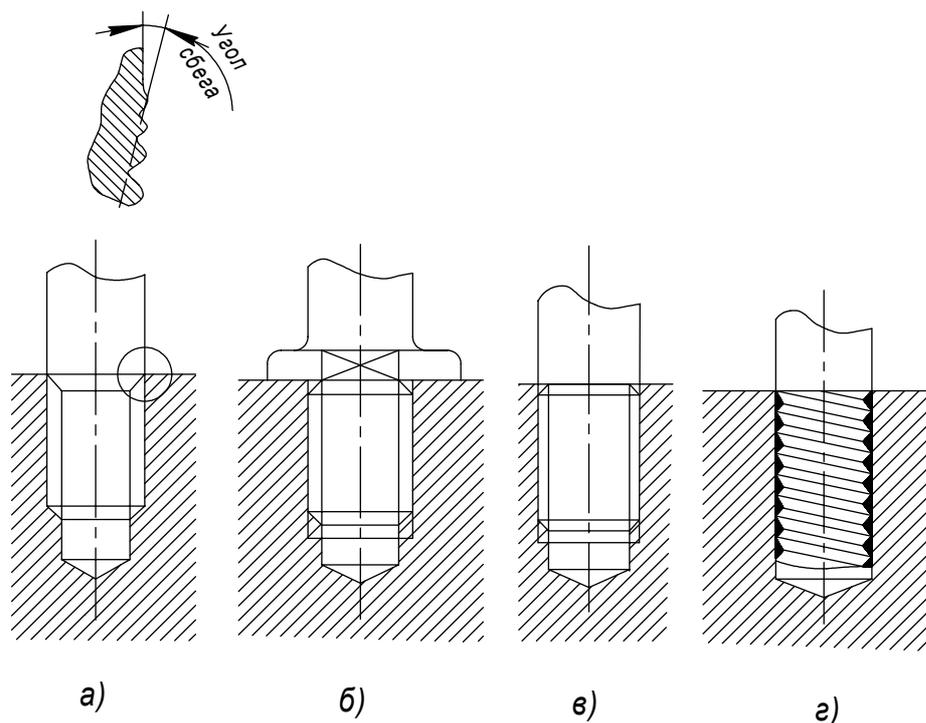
Способы обеспечения неподвижности шпилек в корпусе
